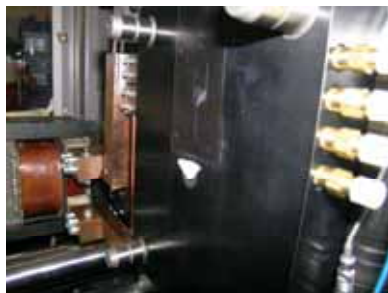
Schließseitige Werkzeughälfte des Testwerkzeuges
